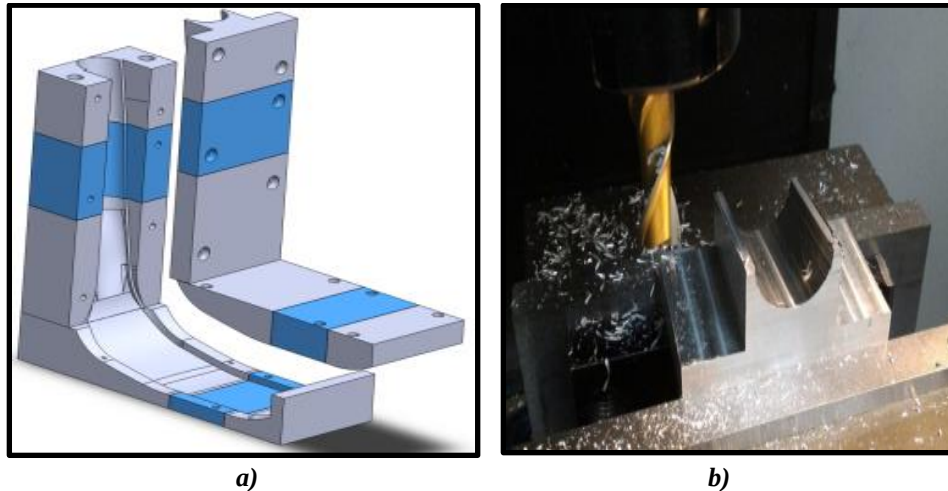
Segundo modelo de molde en aluminio: a) Diseño de molde superior; b) Maquinado de molde en CNC.
